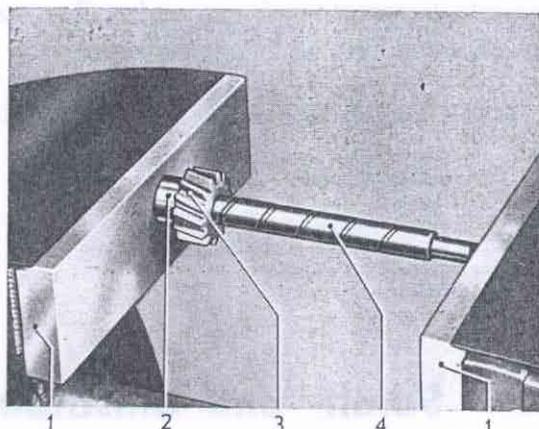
Tachometerschraubenrad mit Aufpreßhülse SW-211 auf Welle aufdrücken
